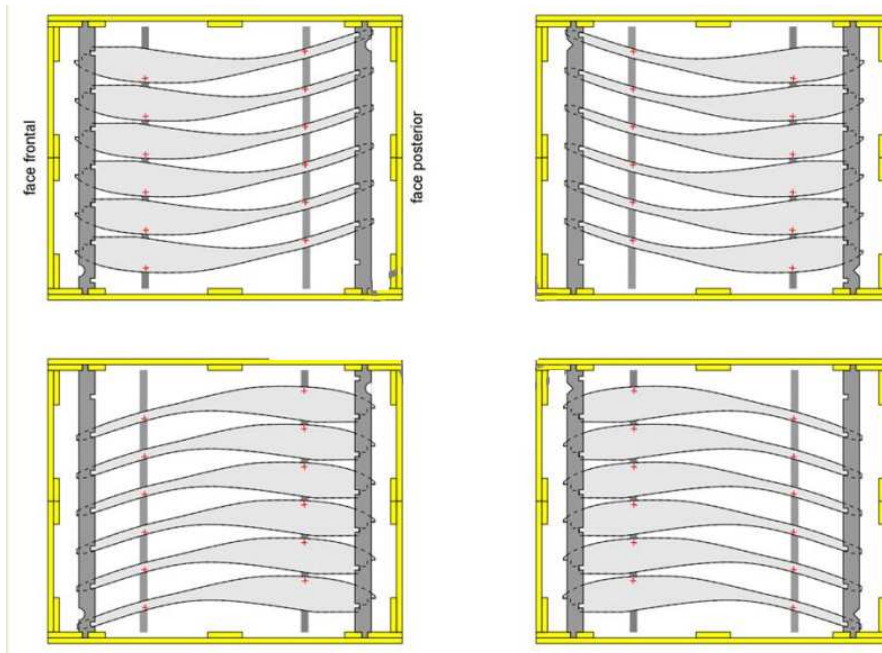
Vista superior da disposição das portas na embalagem de madeira
